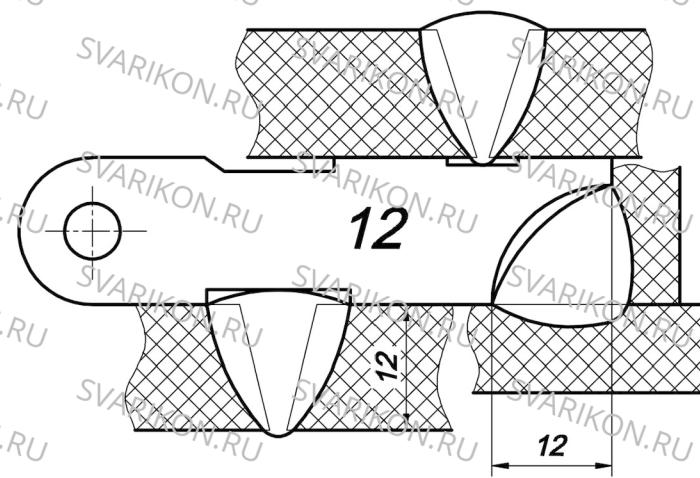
Специальный шаблон для контроля конструктивных элементов сварных швов.
